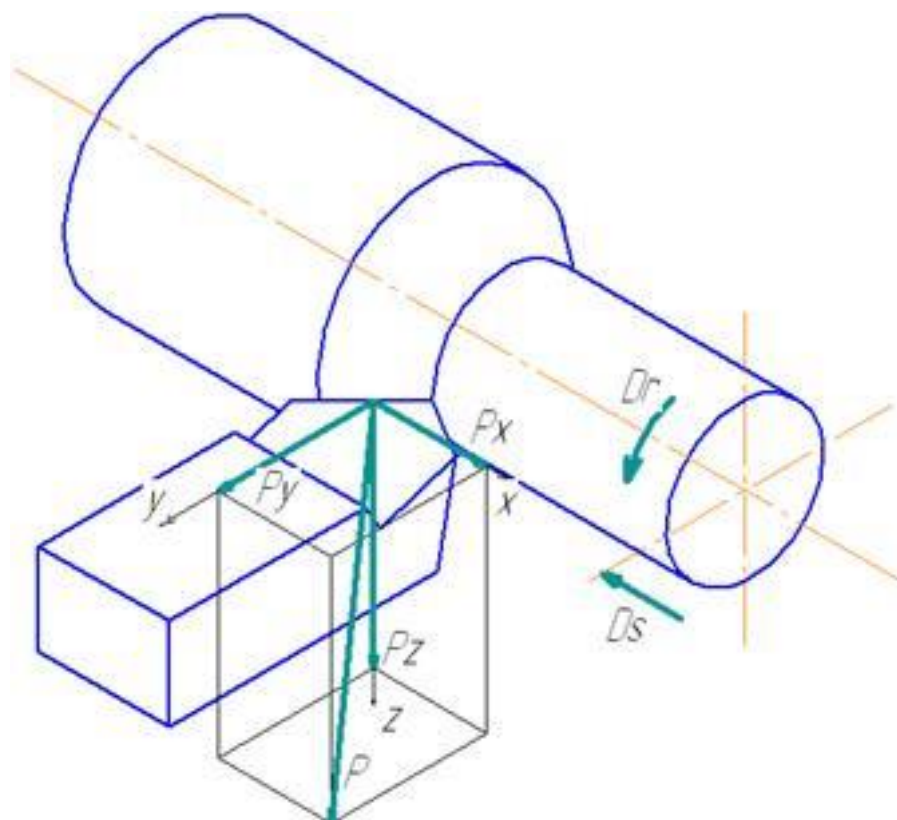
Сили, які діють на інструмент під час обробки деталі
